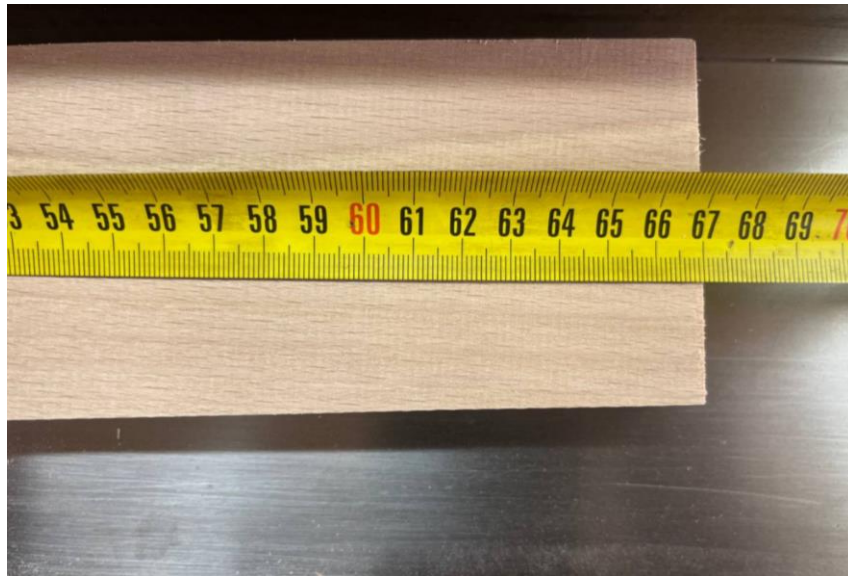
Приклад контрольного вимірювання довжини заготовок після чистового торцювання
